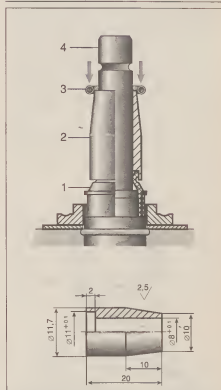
Оправка для монтажа стяжной пружинки: 1 – маслоотражательный колпачок; 2 – оправка; 3 – пружинка; 4 – стержень клапана.
